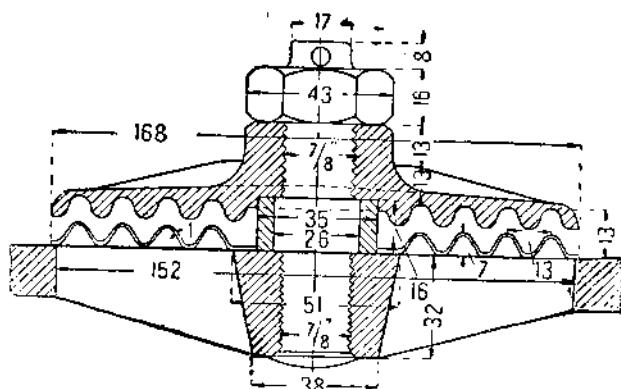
Гибковидный клапан из твердой резины с пружинной нагрузкой.
